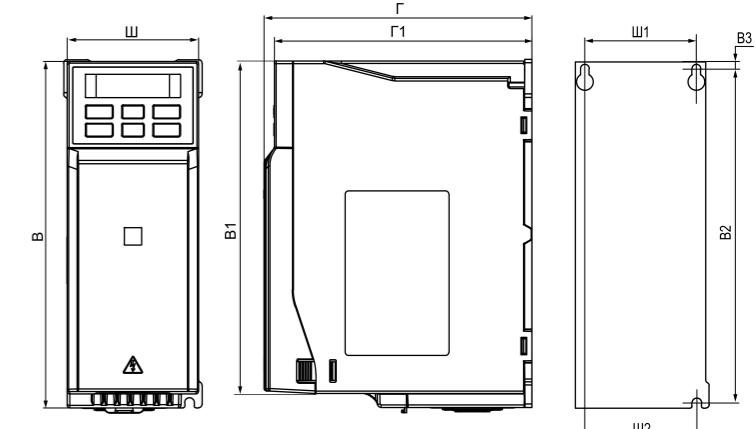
Габаритные размеры прибора в корпусе типоразмера 1
